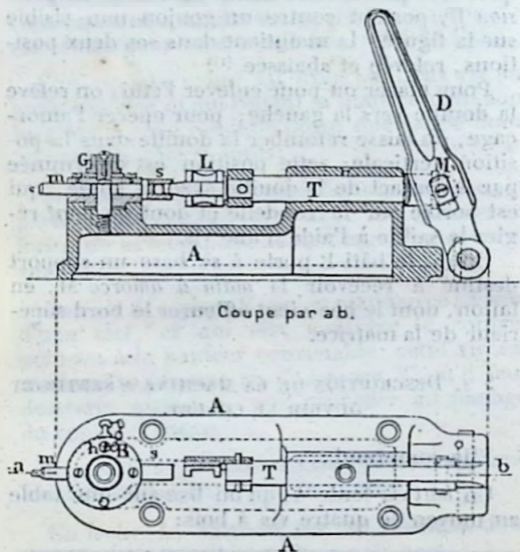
Machine à sertir et à ouvrir le collet (1/5).
